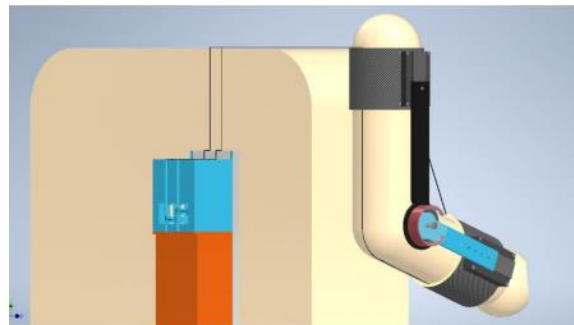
Vista isométrica del diseño final acoplado a la órtesis
